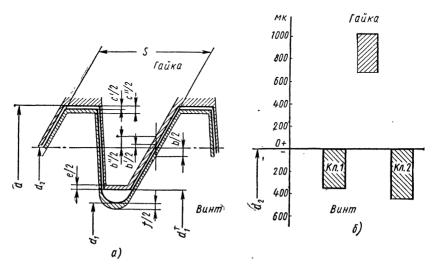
Схема расположения полей допусков на упорную резьбу: $\mathfrak a$ — общая схема; $\mathfrak b$ — допуски по среднему диаметру
